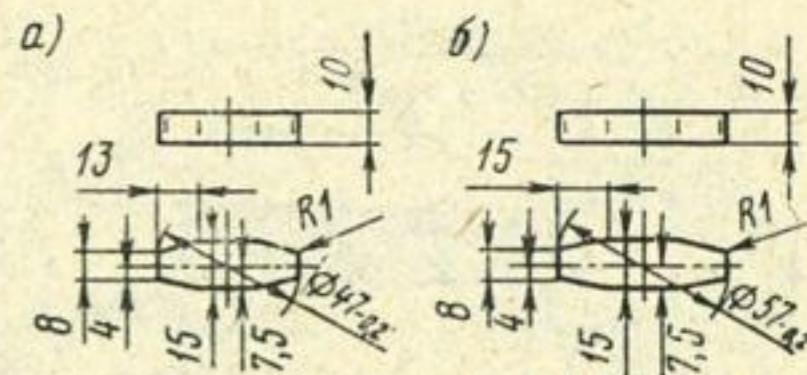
Оправки для выпрессовки наружных колец подшипников ступицы:
